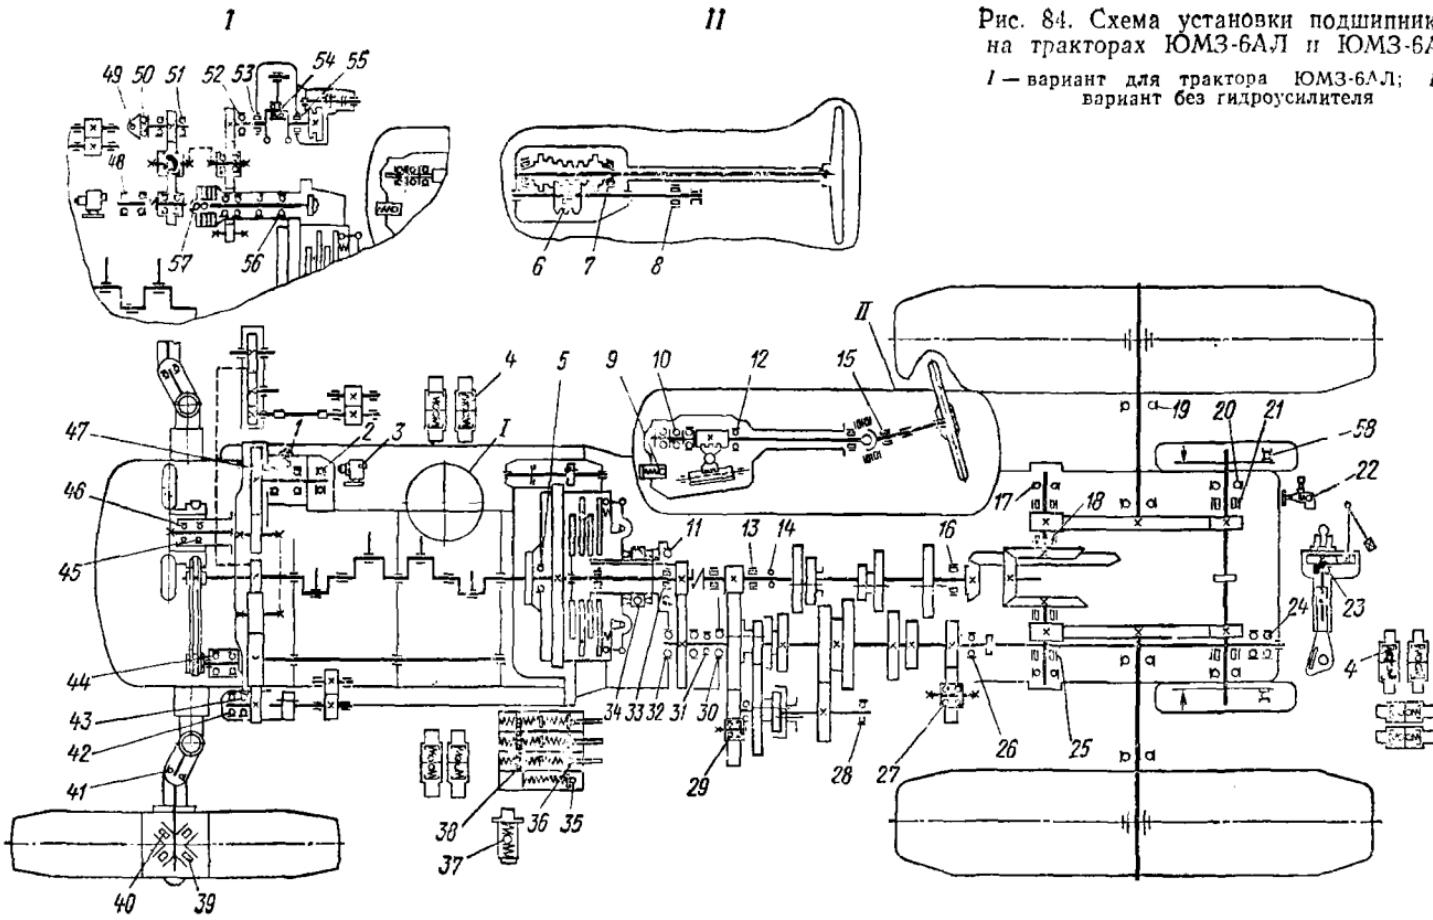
Схема установки подшипников на тракторах ЮМЗ-6АЛ и ЮМЗ-6АМ:
